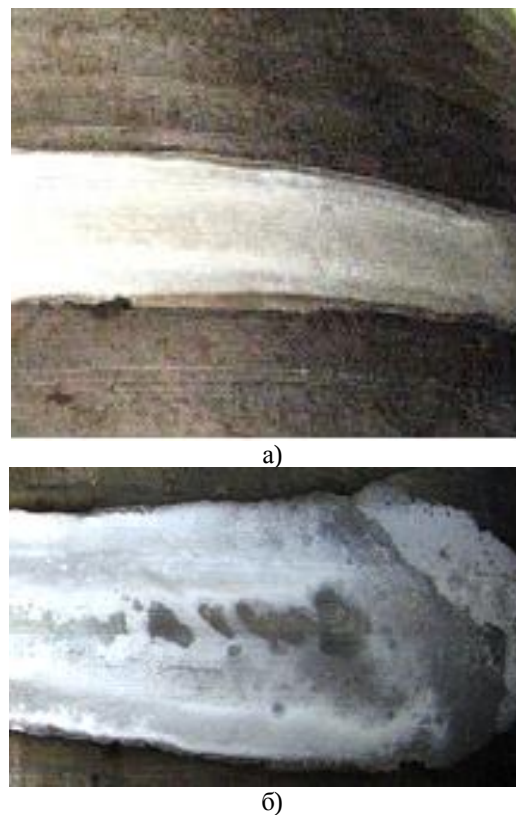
Внешний вид поверхности подвергнутой катодной очистке: а) открытой дугой; б) закрытой дугой
